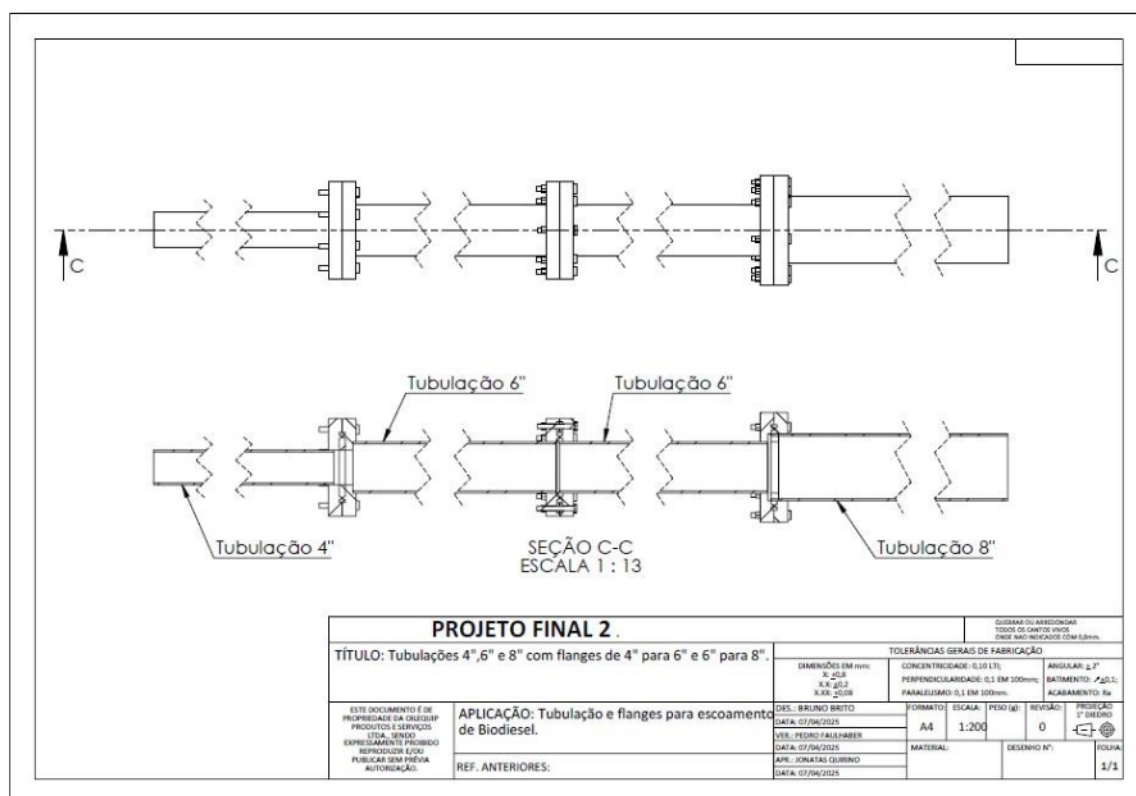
Esquemática de transição 2D de flanges e tubulações (4, 6 e 8 polegadas)
